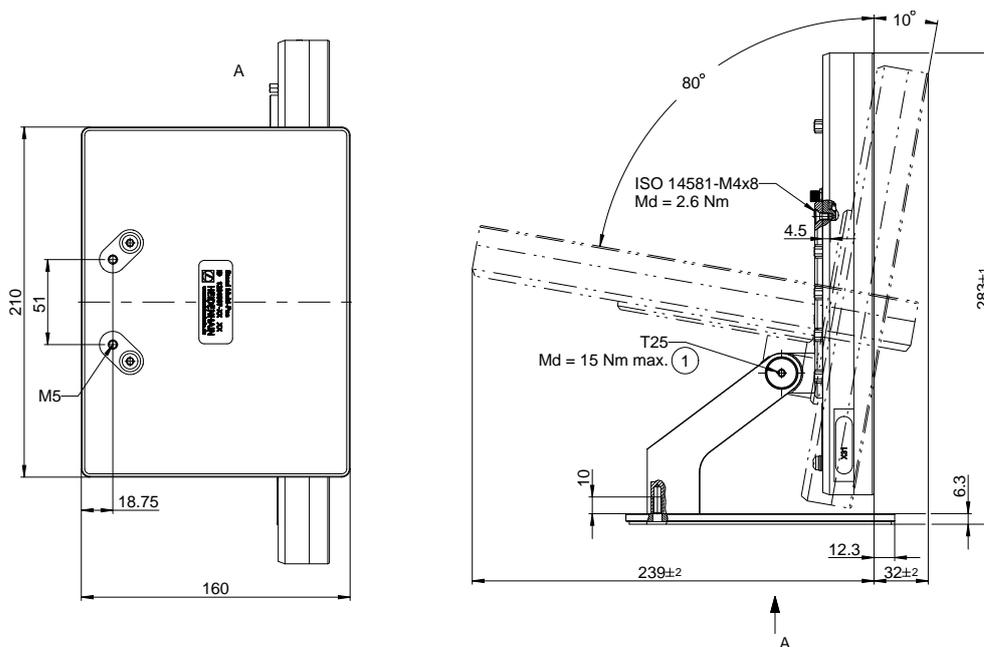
Dimensiones del aparato con pie de soporte Multi-Pos
